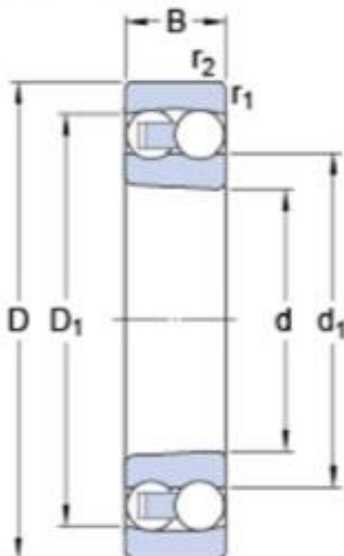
Dimensiones del rodamiento seleccionado para los soportes del tambor.
